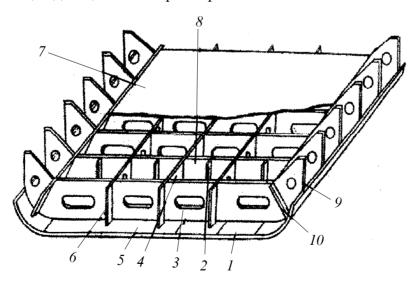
Конструкция днищевого перекрытия с двойным дном при поперечной системе набора:
